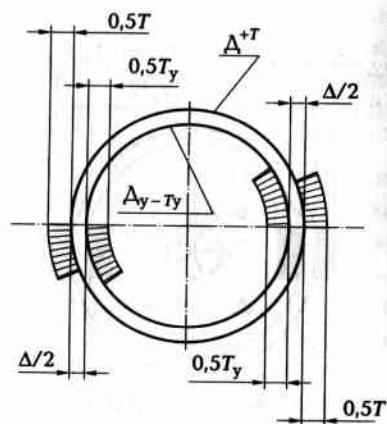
Схема установки детали цилиндрическим отверстием на цилиндрический установочный элемент приспособления
